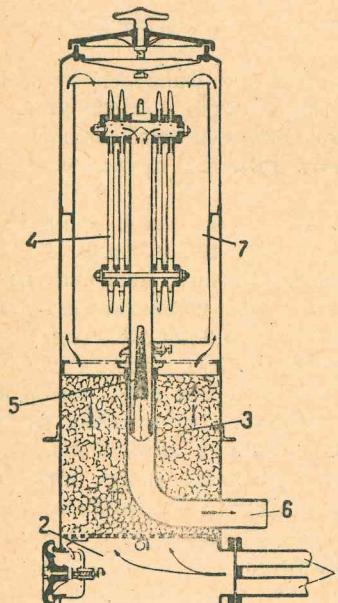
Комбинированный очиститель поверхностной очистки и фильтра конструкции Панар-Левассор с разделенным потоком газа и пыли: 1 — вход грязного газа; 2 — газоприемник; 3 — кокс (поверхностная очистка газа); 4 — фильтры; 5 — фильтр безопасности; 6 — выход чистого газа; 7 — кожух фильтров
